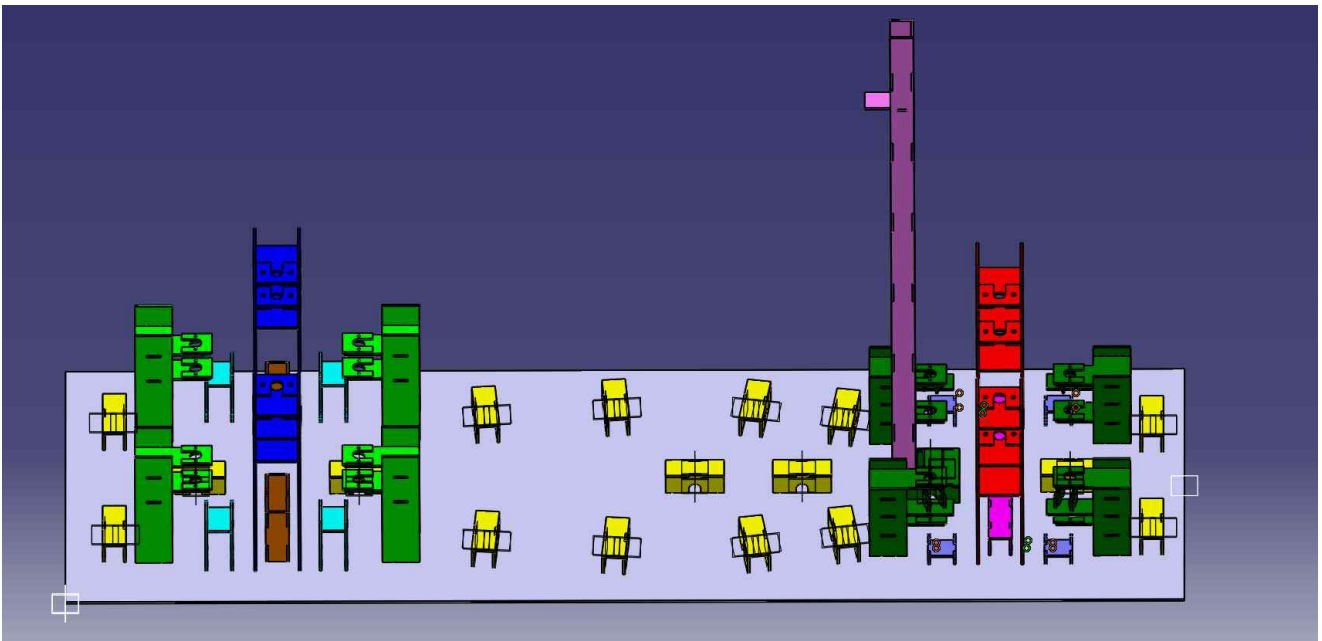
프레임 철판 지그 3D Assembly 파일 캡처본
